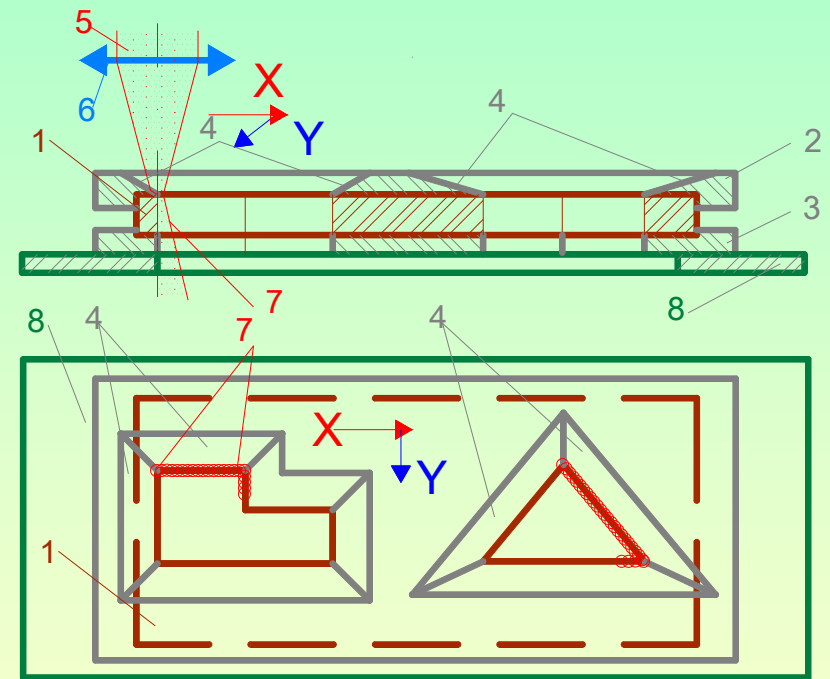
Схема обробки та приладдя для вирізання прямокутних вікон (пазів)
